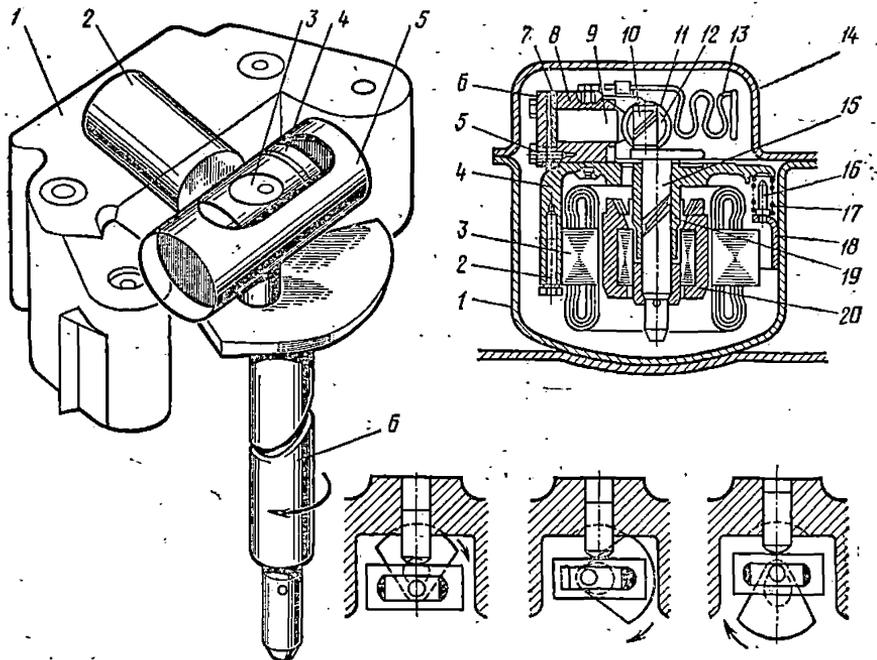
Кулисный механизм герметичного компрессора ФГО,1:
